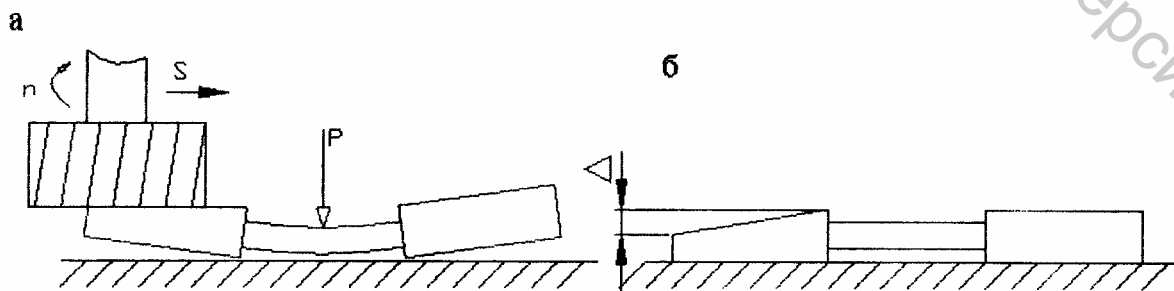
Заготовка при обработке (а) и после закрепления (б)
